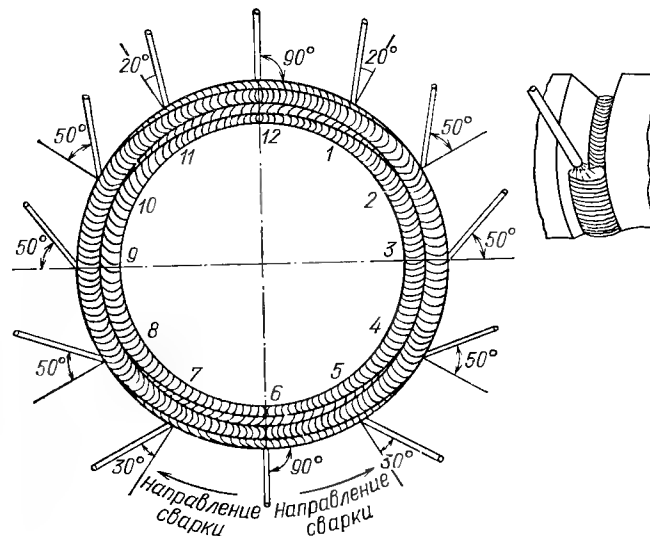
Схема сварки неповоротного вертикального стыка слоями повышенной толщины.
